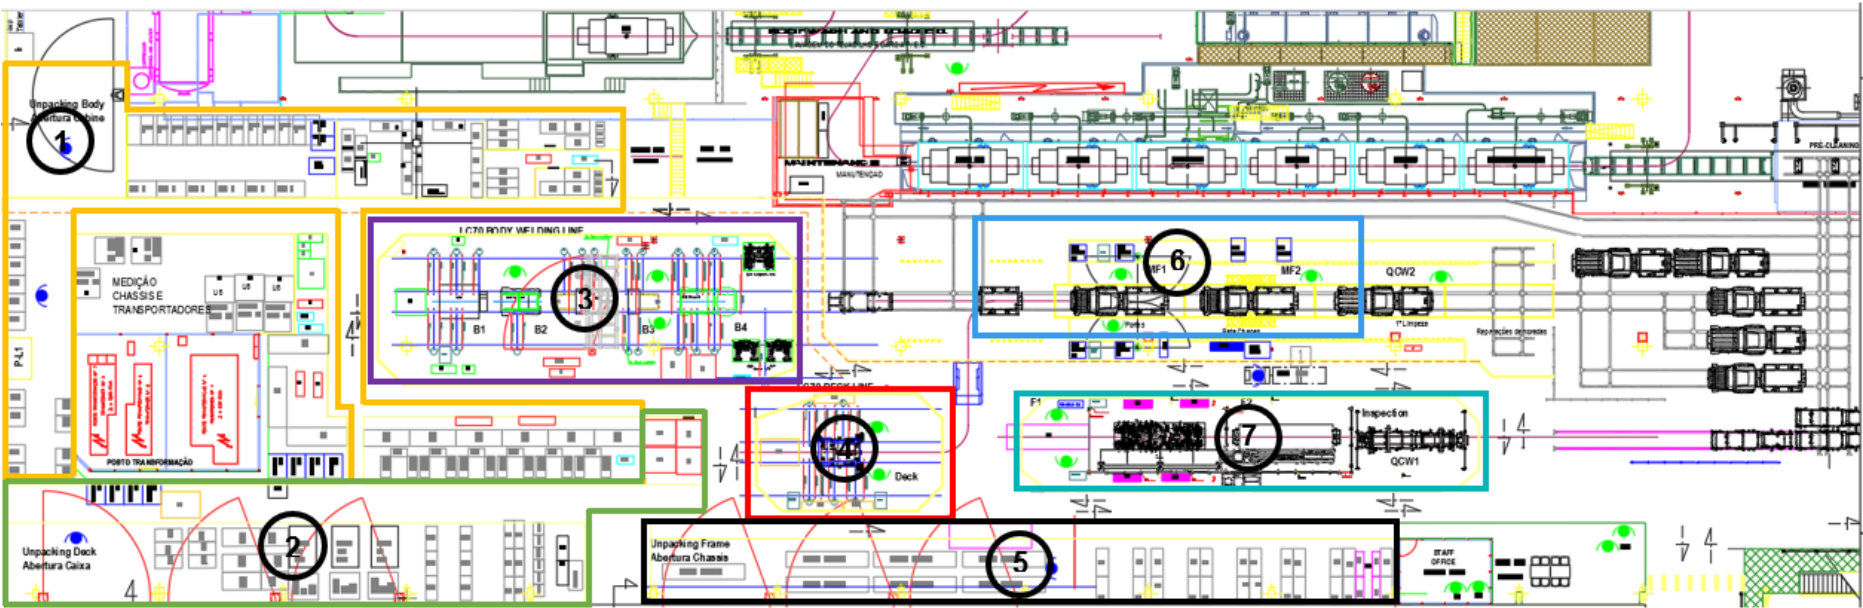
Layout Armazém área de Soldadura (Fonte: Adaptado de Toyota Caetano Portugal)
